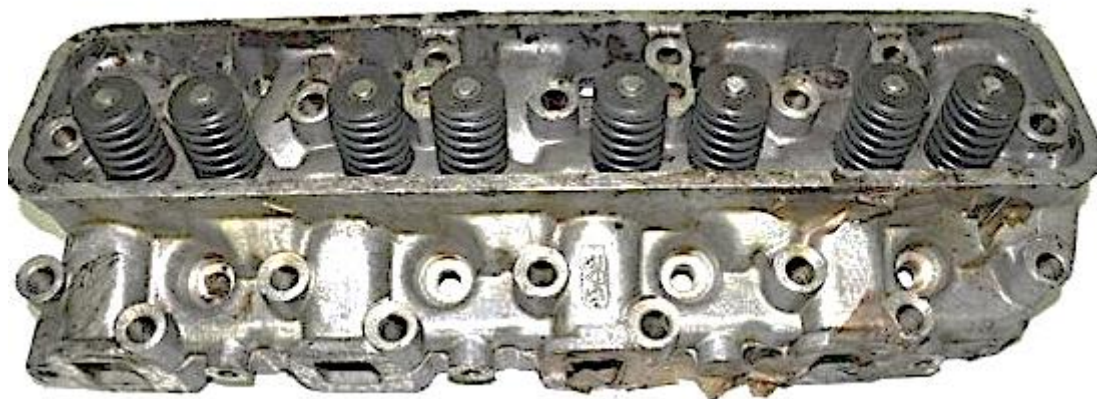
Головка блока цилиндров ГАЗ-53
